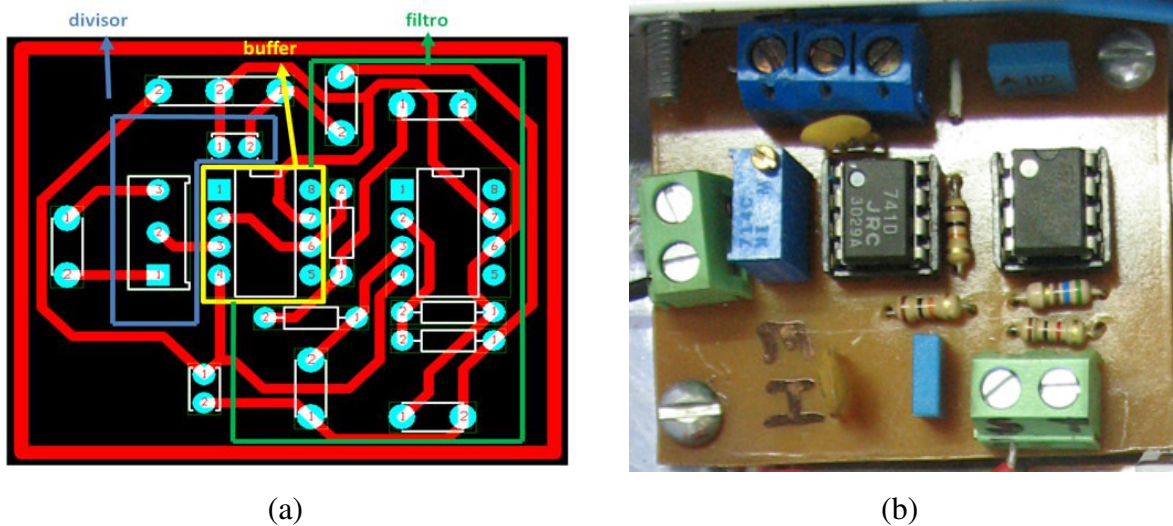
Circuito elétrico do condicionador de sinal do efeito Hall. (a) Projeto da placa de circuito impresso e (b) placa com os componentes instalados
